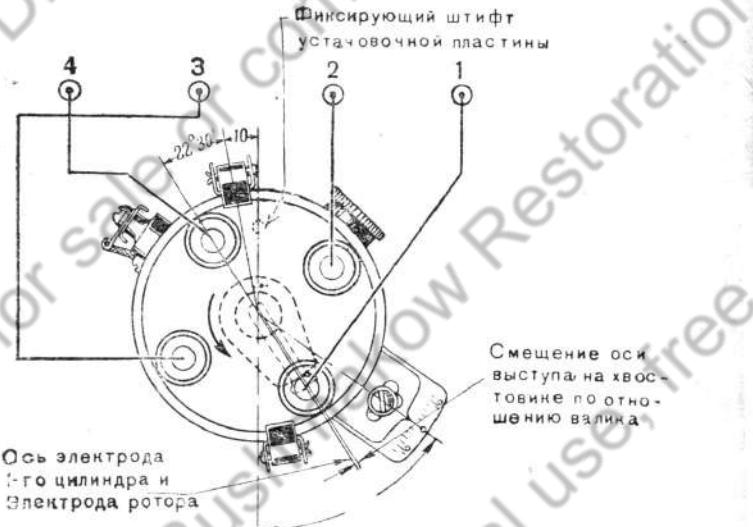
Расположение установочных деталей прерывателя-распределителя P-15
